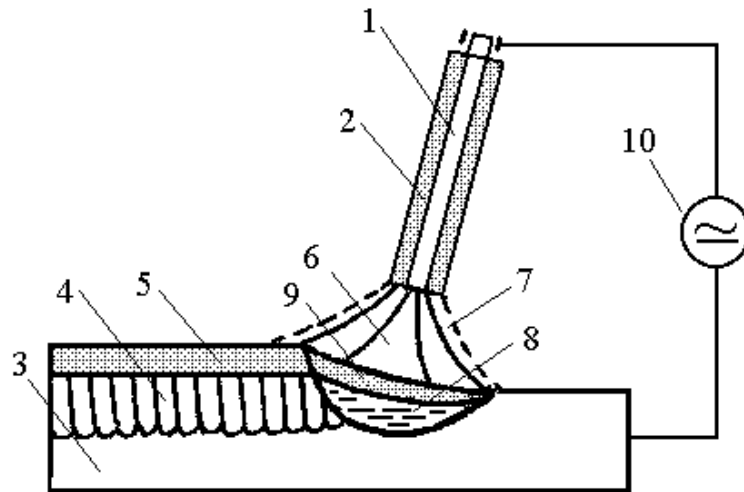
Схема ручной дуговой сварки плавящимся электродом с покрытием:
